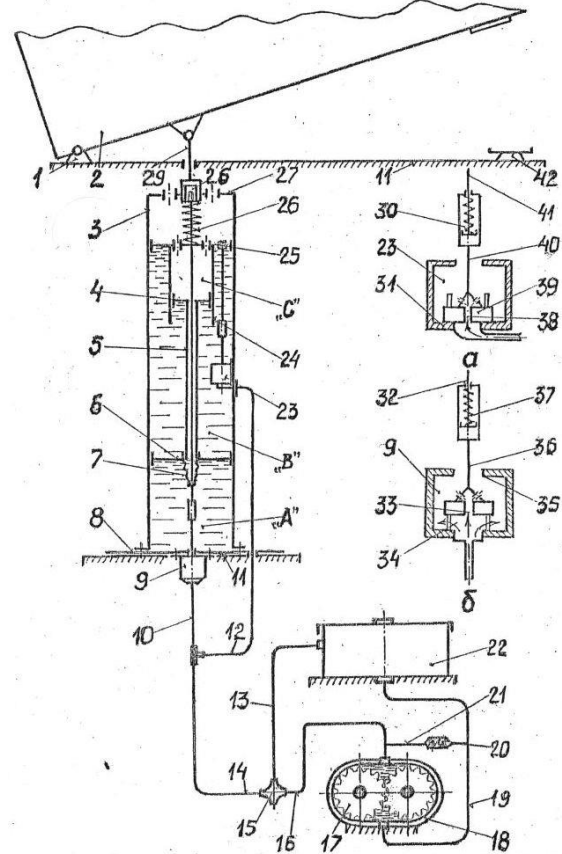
Принципиальная схема гидропривода подъемного механизма кузова самосвала: а – схема первого дозатора; б – схема второго дозатора; 1 – шарнир; 2 – кузов; 3 – корпус; 4, 6, 25 – поршни; 5, 32, 36, 40, 41 – тяги; 7 – чехол; 8 – фланец; 9, 23 – дозаторы; 10, 12, 13, 14, 16, 19, 21 – гидролинии; 11 – рама; 15 – кран; 17 – насос; 18 – источник давления гидропривода; 20, 34, 39 – клапаны; 22 – бак; 24 – направляющая; 26, 30, 37 – пружины; 27 – крышка; 28 – гайка; 29 – шток; 31, 35 – седло; 33, 38 – дроссели; 42 – упор
